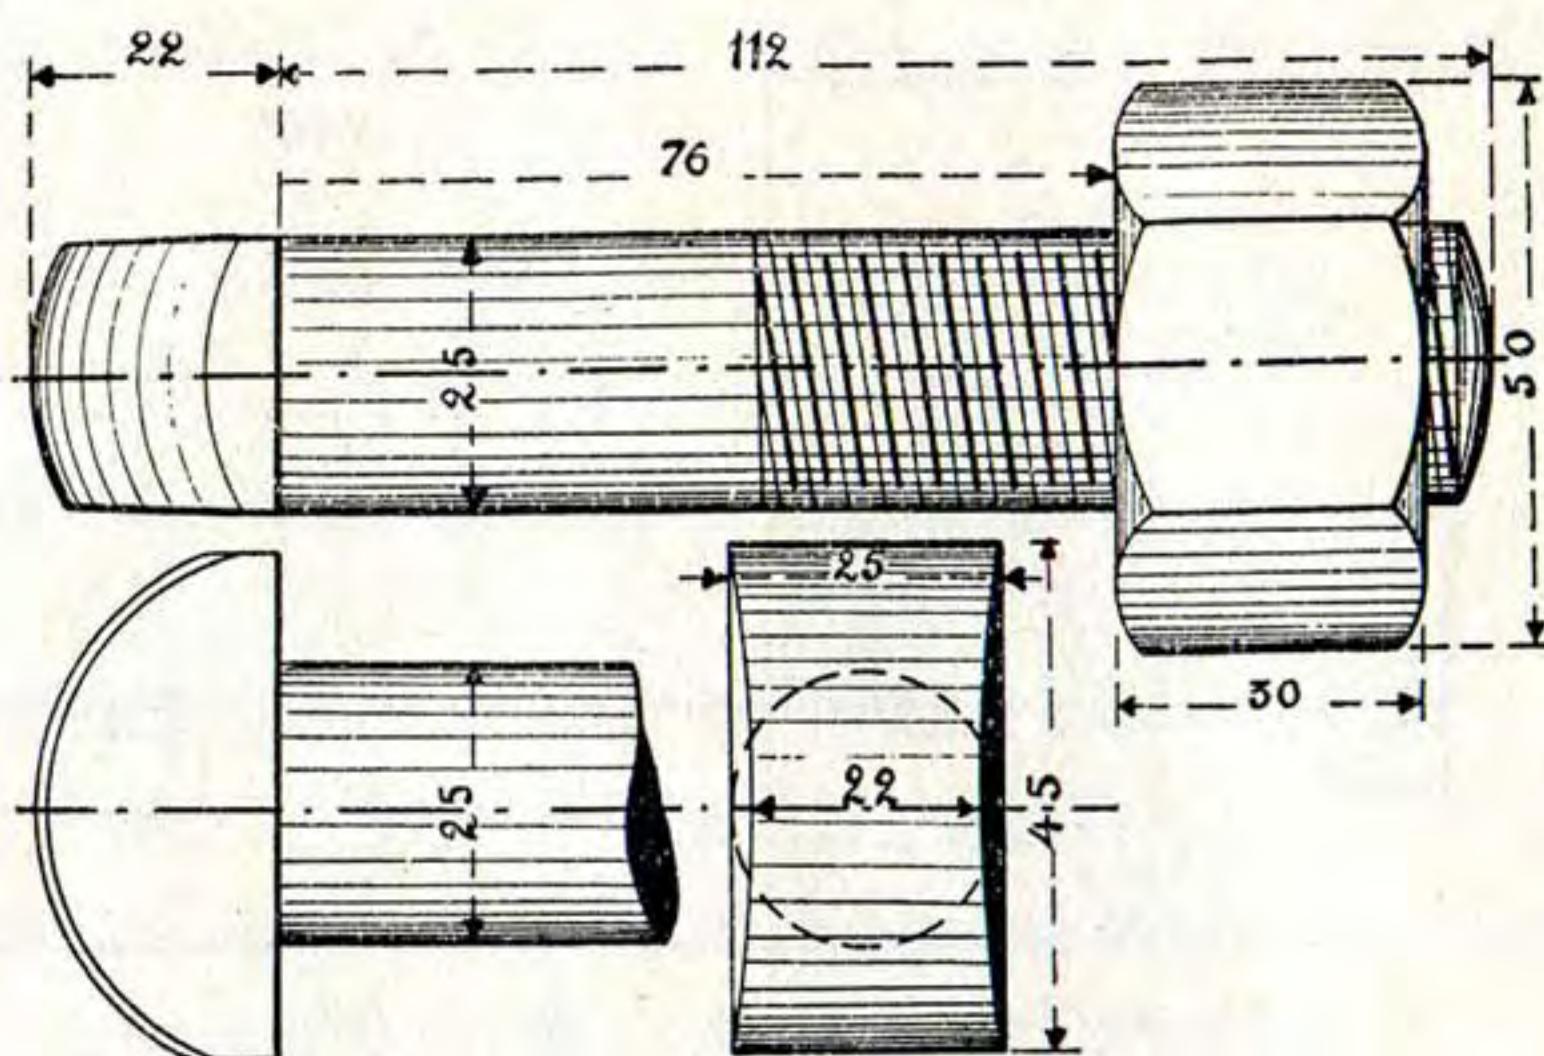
Laschbout voor rail van 52 kgr. Halve grootte.
